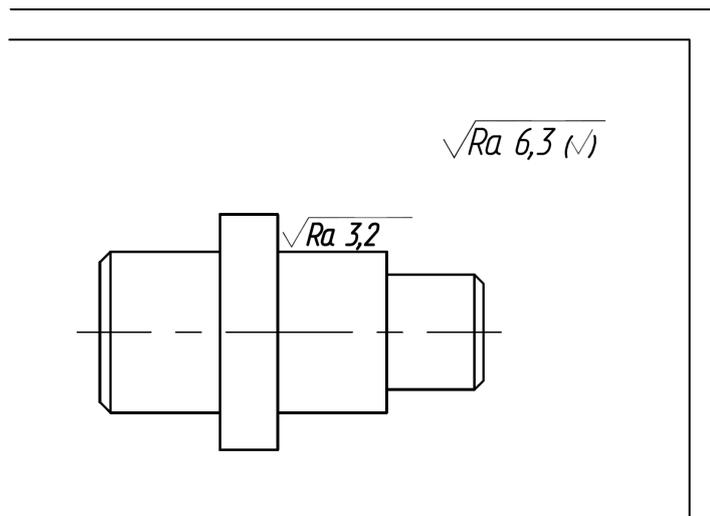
Обозначение общей шероховатости поверхностей, кроме указанной на изображении детали
